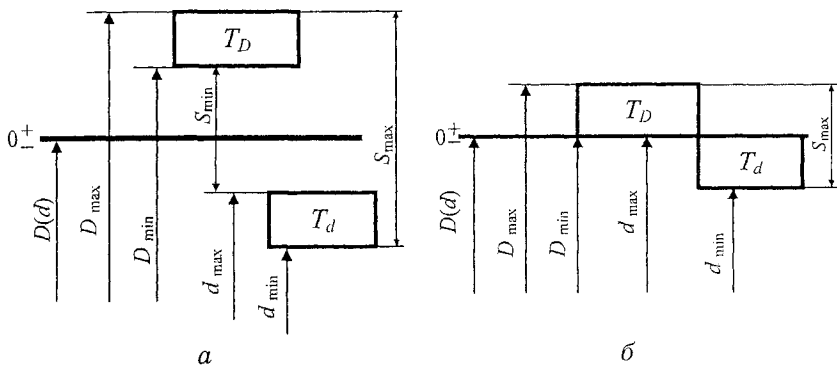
Примеры расположения полей допусков посадок с зазором
